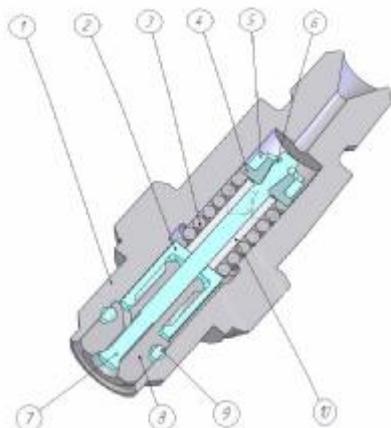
Клапанная форсунка: 1- корпус форсунки; 2-гайка регулировочная; 3-пружина; 4-сухарь; 5-втулка; 6-фиксатор; 7-игла; 8-корпус распылителя; 9-кольцо уплотнительное; 10- втулка дистанционная
